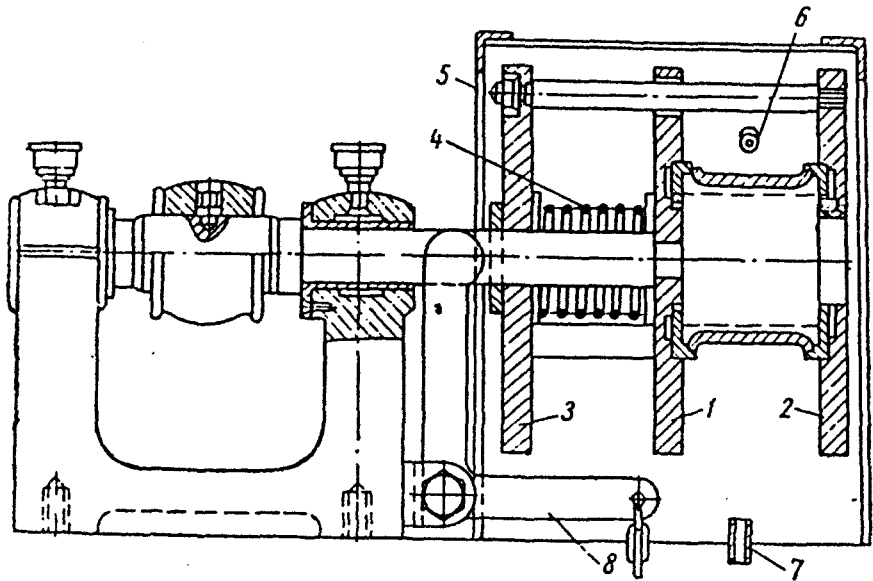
Приспособление для центробежной заливки подшипников:
